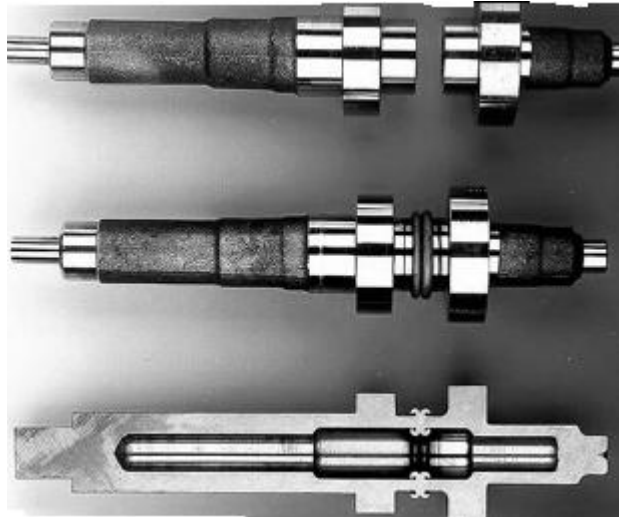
(d) Soudage de tige de piston.
